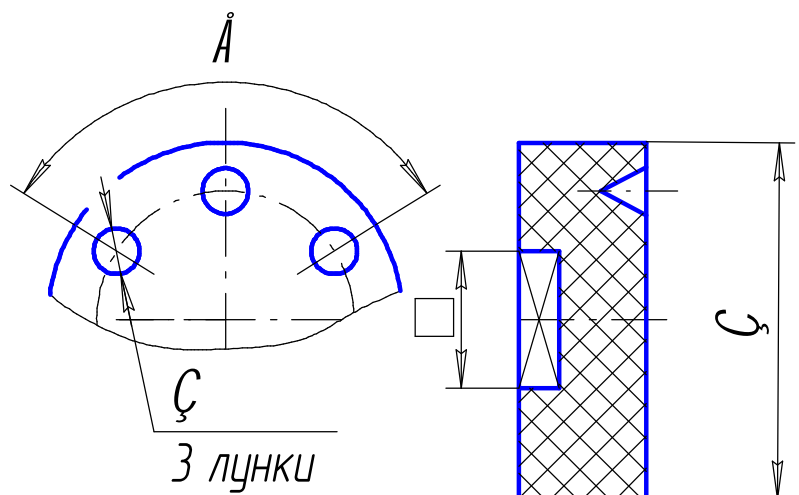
Чертеж клапана с неравномерно расположенными углублениями.
